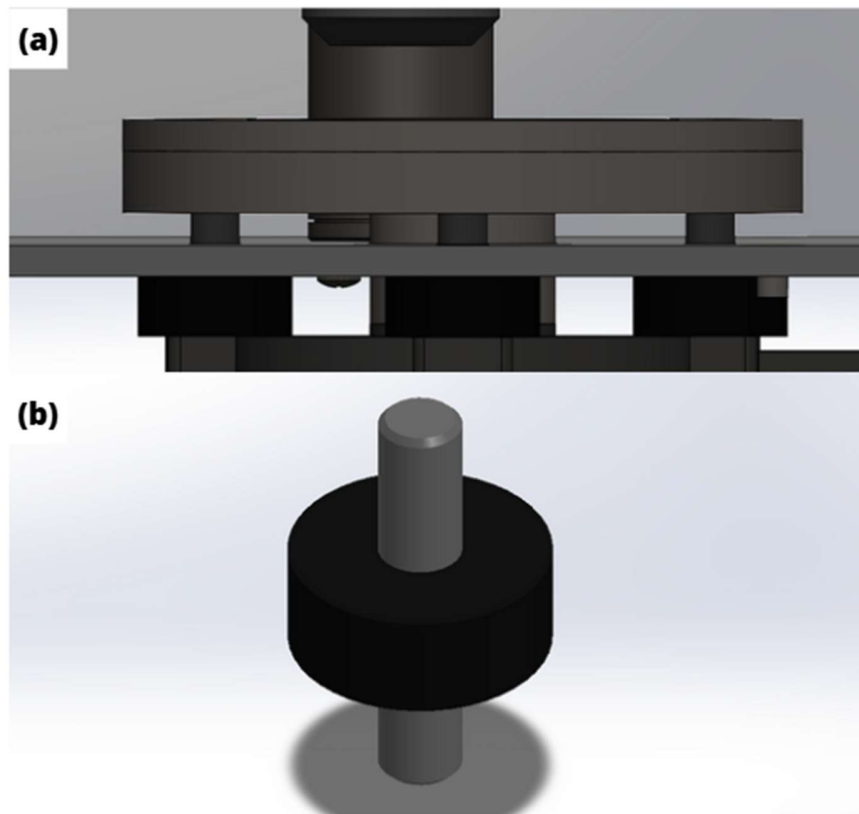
Unión del motor a la máquina a) Motor unido a la lámina mediante soportes de goma con rosca M8 b) soporte de goma con rosca M8 para unión del motor con la lámina.
